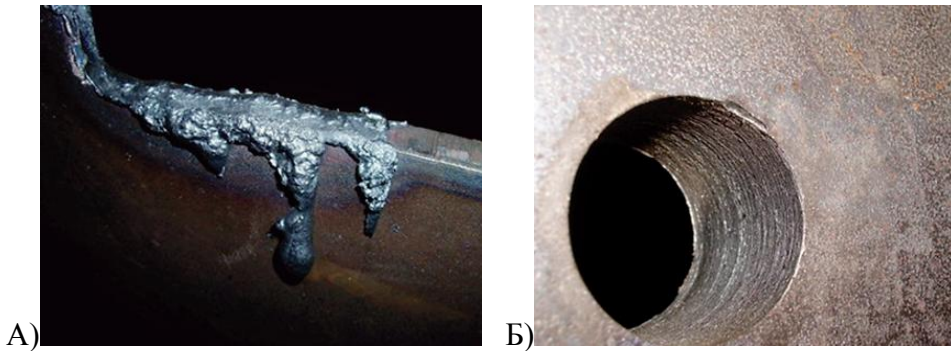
А – Грот, окалина, капли металла от газовой резки, 5Б – Острые кромки отверстий после сверления
